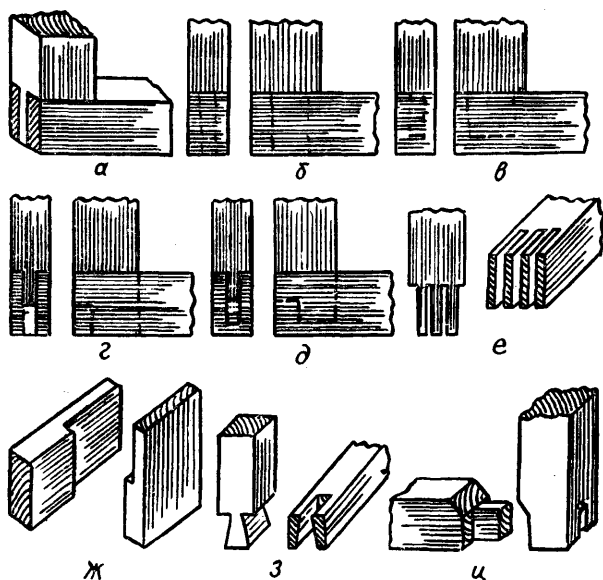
Соединения, применяемые для формирования рамок из брусков с прямоугольной подрезкой:
